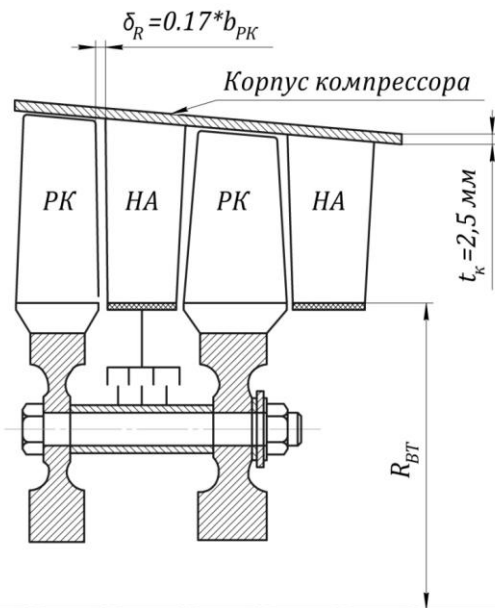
Схема ступеней компрессора с крепежными элементами и корпусом
